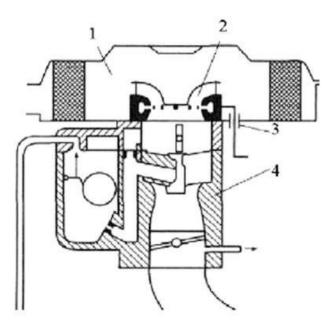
Схема подачи газа над карбюратором: 1 - воздушный фильтр: 2 - смеситель-насадка; 3 - отверстие для подвода газа: 4 - корпус карбюратора
